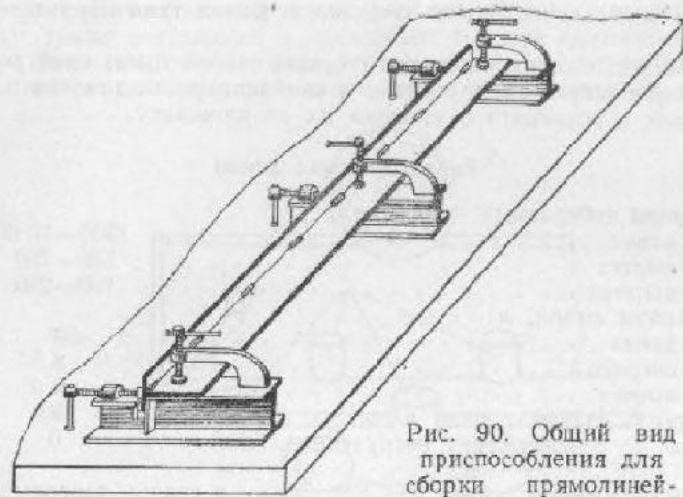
Общий вид приспособления для сборки прямолинейных тавров.
